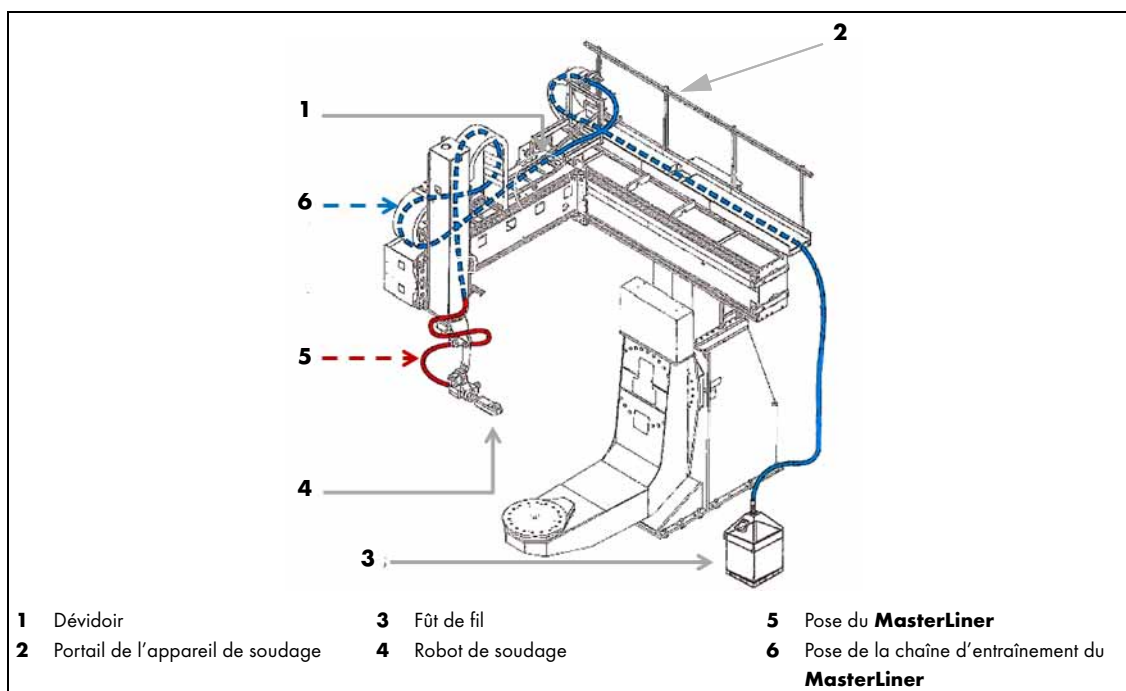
Pose des éléments de soudage robotisé
